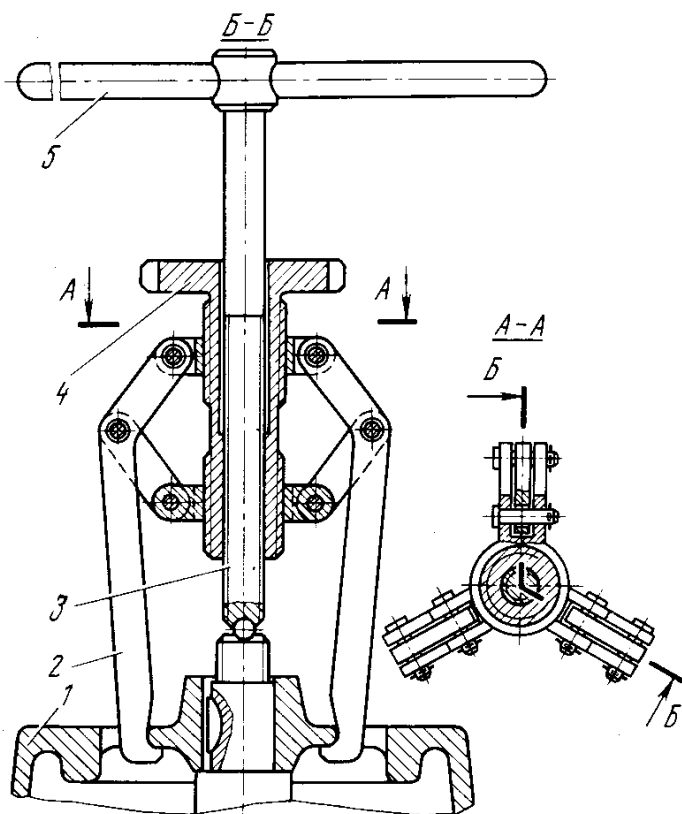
Съемник рабочего колеса вентилятора: 1 — рабочее колесо вентилятора; 2 — лапка; 3 — винт; 4 — втулка с маховиком; 5 — вороток
